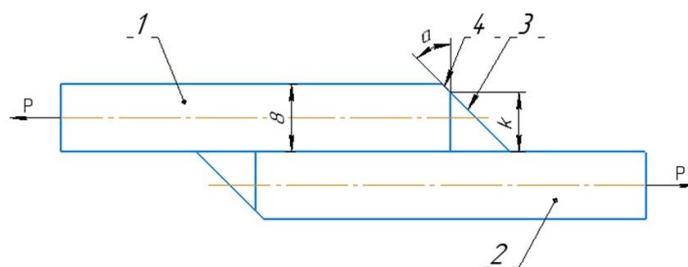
Усовершенствованное сварное нахлесточное соединение
